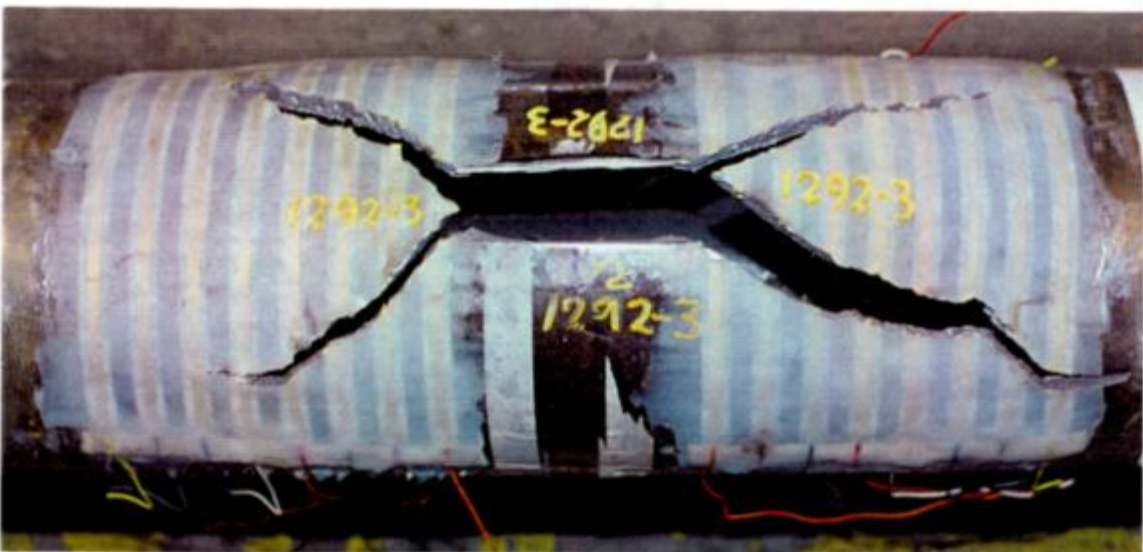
Aspecto general de la fractura en la probeta T 1292-3.
